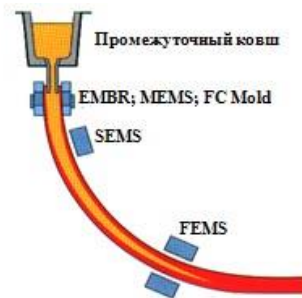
Електромагнітний вплив при формуванні безперервнолитої заготовки
